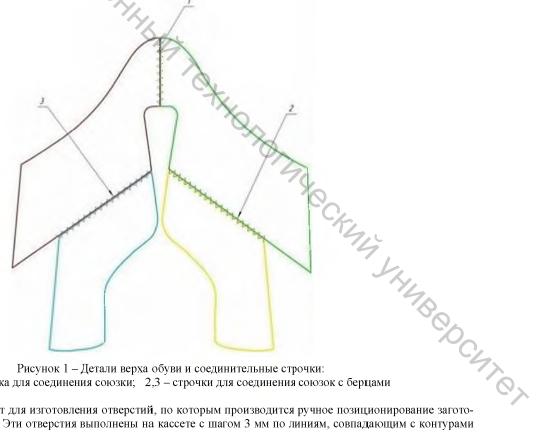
Детали верха обуви и соединительные строчки: 1 – строчка для соединения союзки; 2,3 – строчки для соединения союзок с берщами
